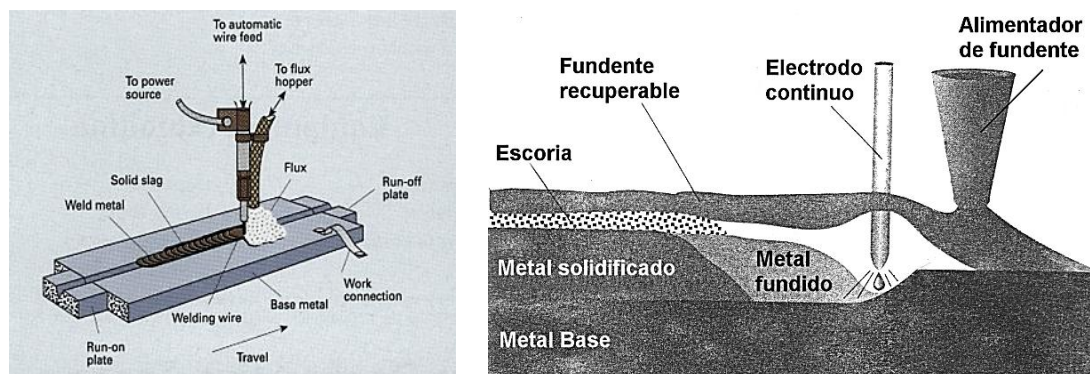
Esquema de soldadura por arco sumergido [17, 18].
